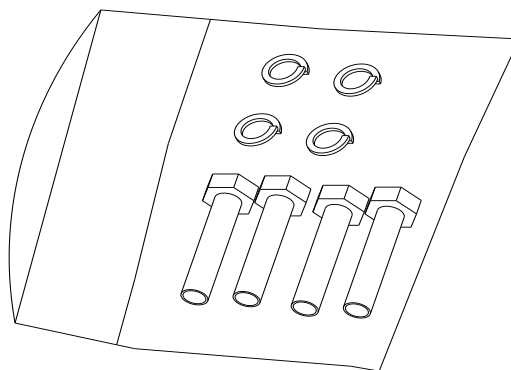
15 Sechskantschrauben (M8×30) und Federringe
